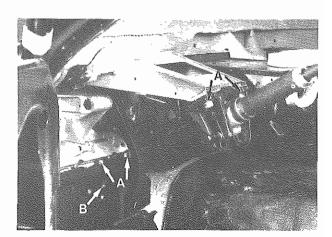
A - Viti fissaggio piantone al lelaio Screws fixing steering column to frame
